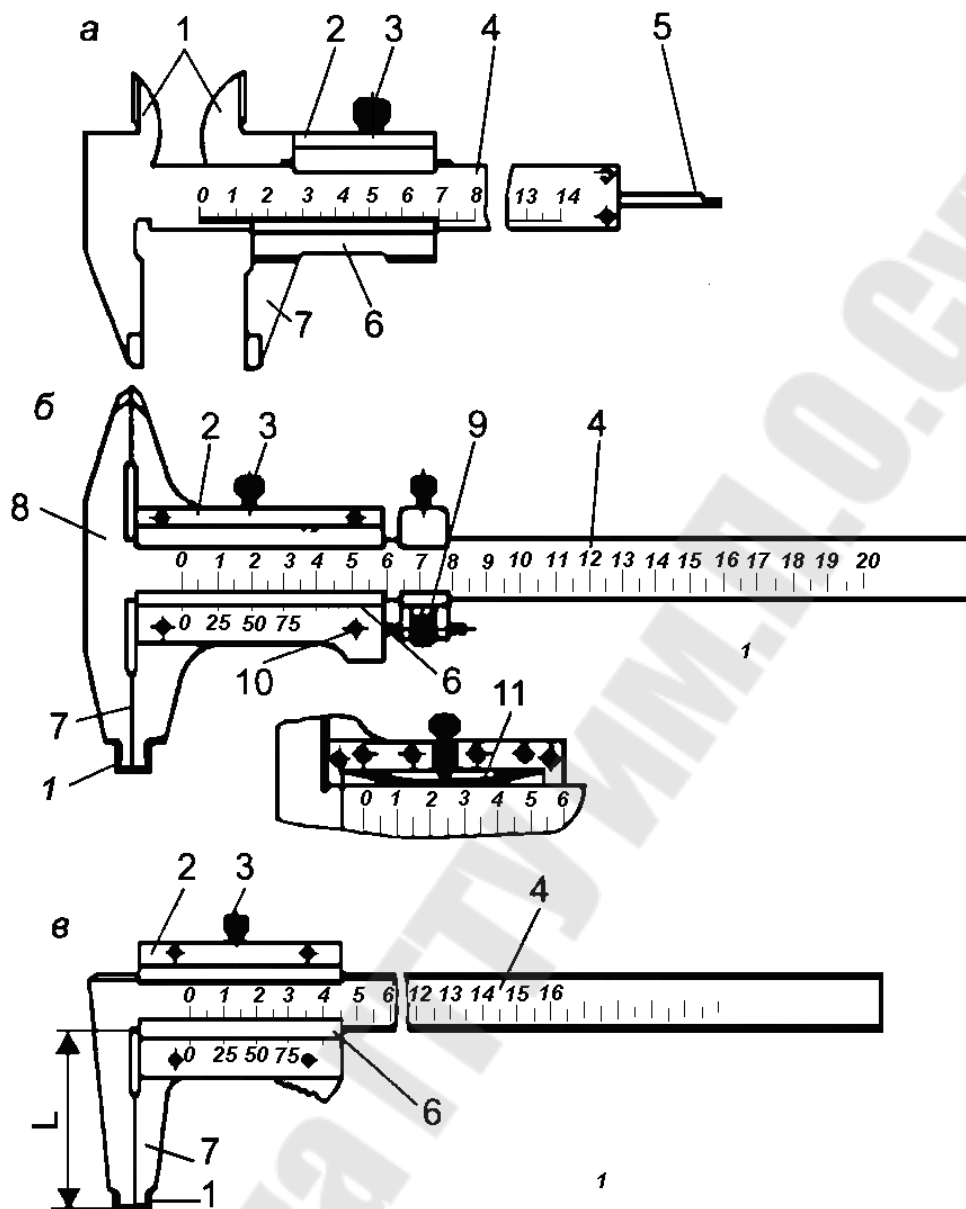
Штангенциркули: а) ШЦ-I; б) ШЦ-II; ШЦ-III: 1- губки для внутренних измерений; 2 – рамка; 3 – винт стопорный; 4 – штанга; 5 – ножка глубиномера; 6 – нониус; 7 – губки для наружных измерений; 8 - разметочные губки; 9 – гайка микроподачи; 10 – винты для крепления нониуса; 11- пружина.
